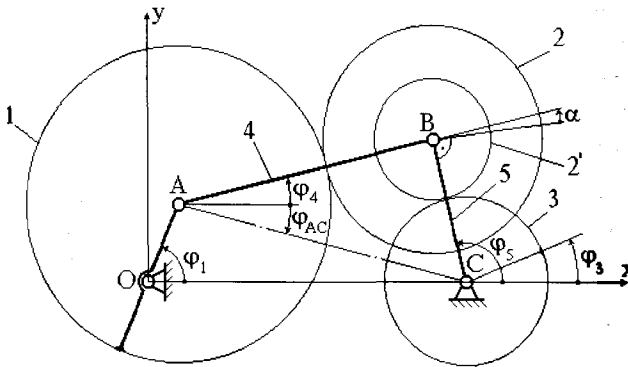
Простейший ЗРМПД с круглыми зубчатыми колесами
